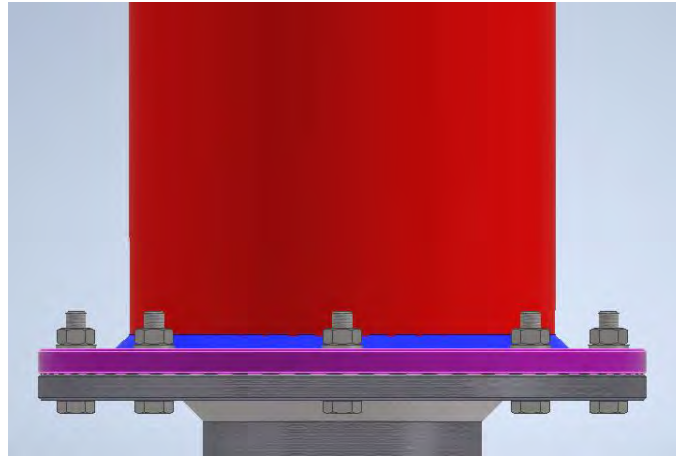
Soldadura entre la carcasa y la plancha de soporte de la carcasa.
